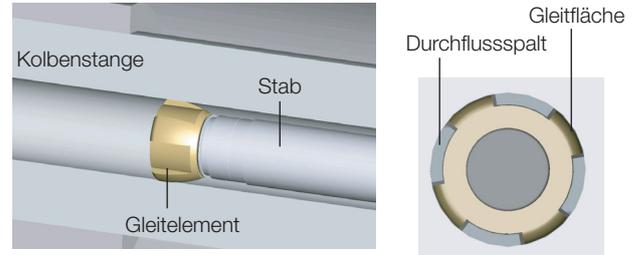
Detailansicht und Draufsicht Gleitelement
